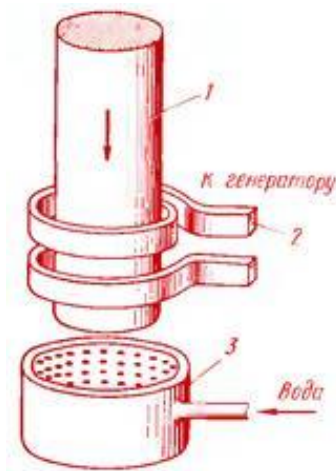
Расположение индуктора, закаливаемой цилиндрической детали и спрейера при закалке с нагревом ТВЧ:
